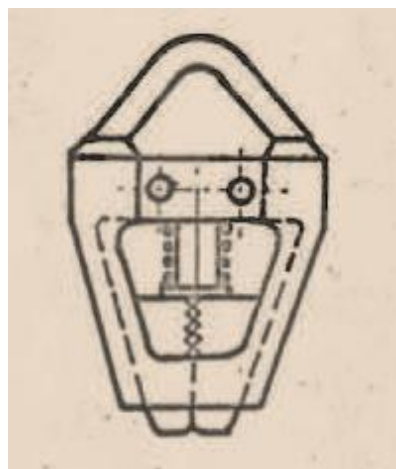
Perro utilizado normalmente en la empresa Trefilerías Quijano.
